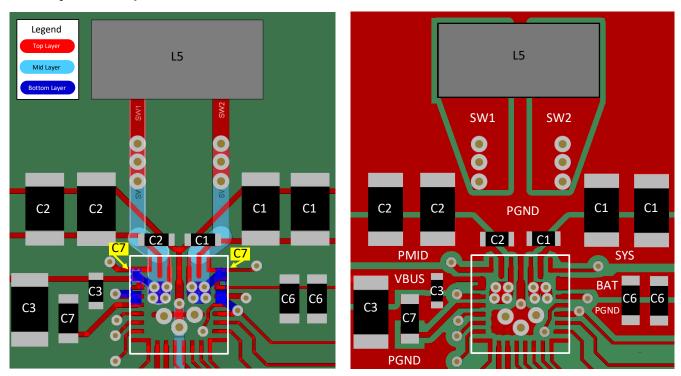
PCB Layout Example (Top Layer Copper Pours Removed on Left, Shown on Right)
